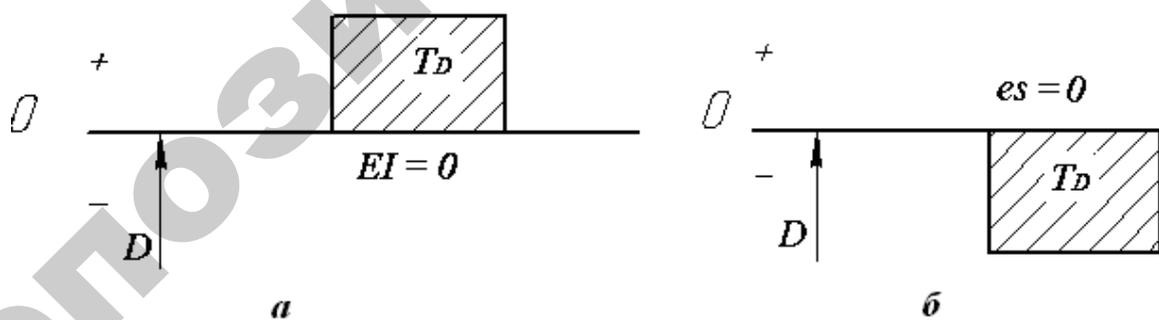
Расположение поля допуска основной детали:
